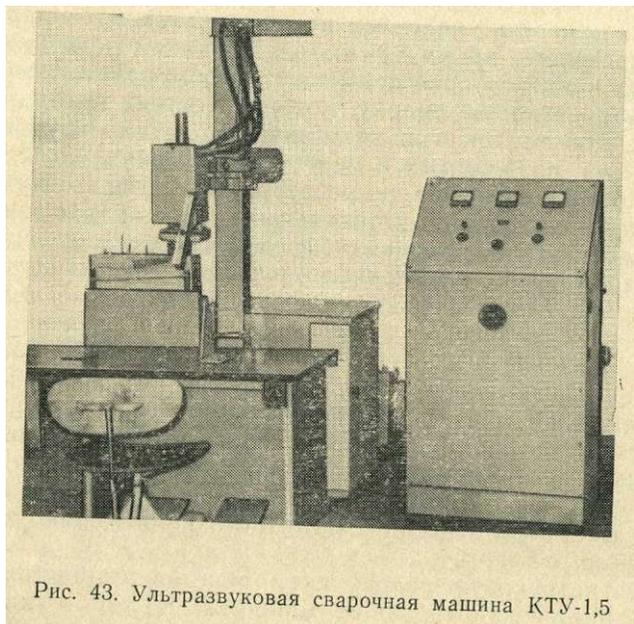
Ультразвуковая сварочная машина КТУ-1,5
